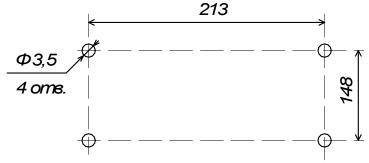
Размеры под сверление отверстий в панели для установки БАО
